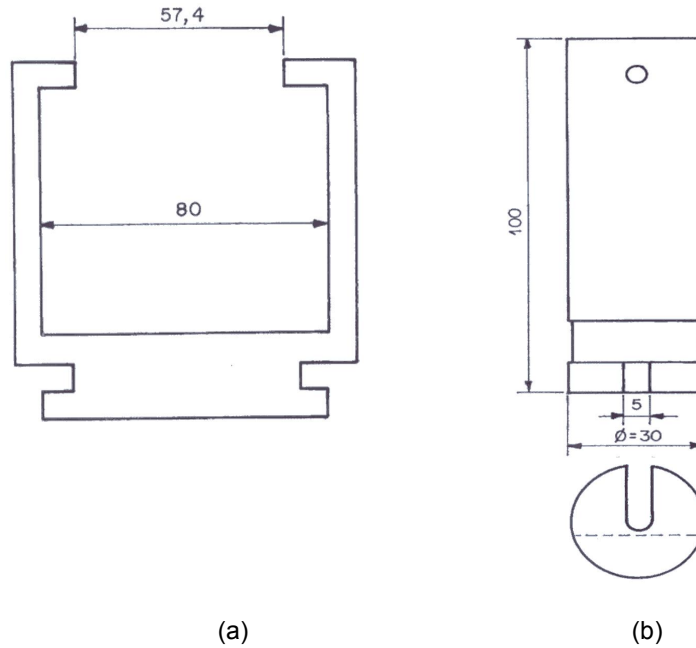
(a) Dispositivo para fixar a amostra, dimensões em milímetros. (b) Dispositivo para tracionar o parafuso, dimensões em milímetros.
